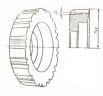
Конструктивные параметры задней поверхности полбяков. когда эта поверхность является пилиндрической
